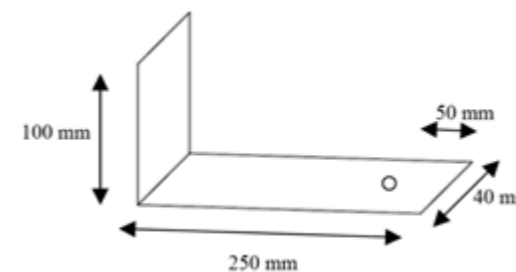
Het regelprofiel 100/250/40 - voorzien van 4 voorgeboorde gaten van 9mm voor de bevestiging van de draagstructuur.
